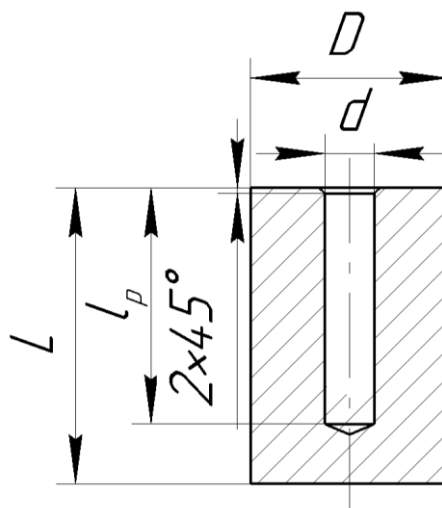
Образец втулки с глухим глубоким отверстием для обработки резьб М5
